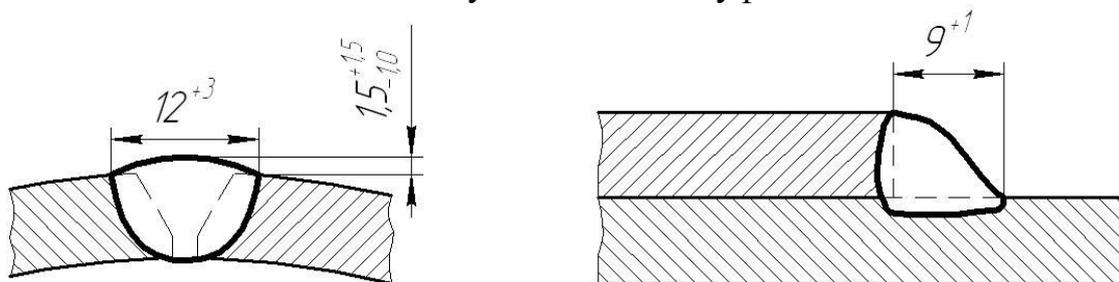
Размеры сварного соединения продольных и кольцевых швов
